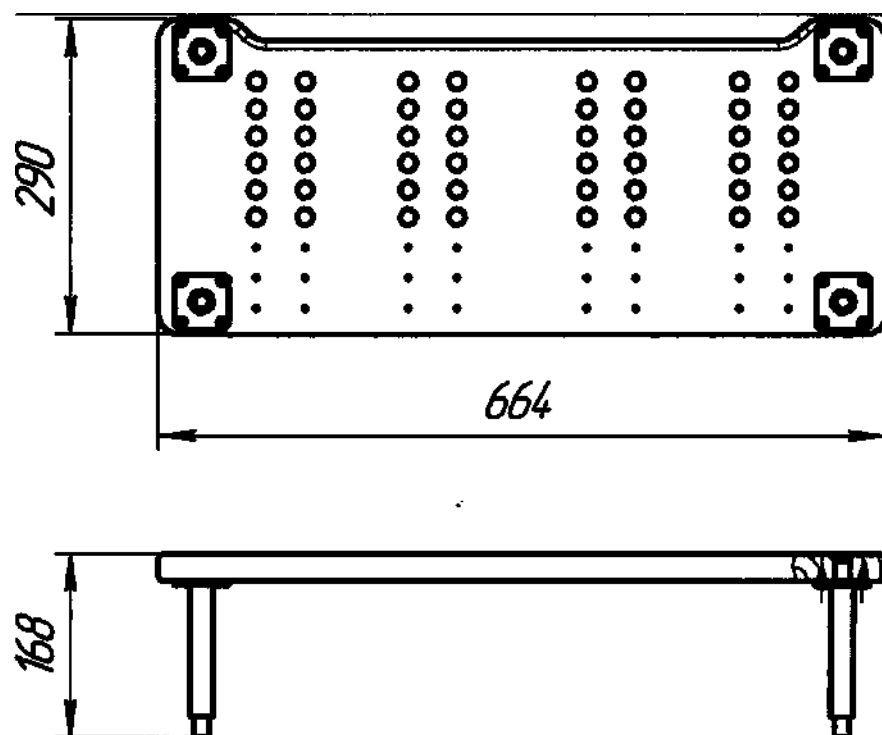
Габаритные размеры дополнительной опоры для ног
